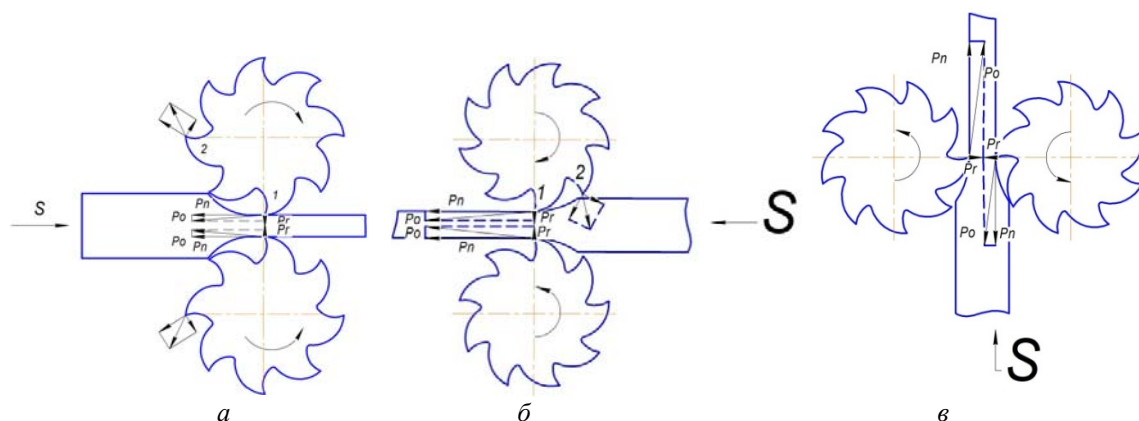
Возможные схемы обработки оппозитными фрезами:
